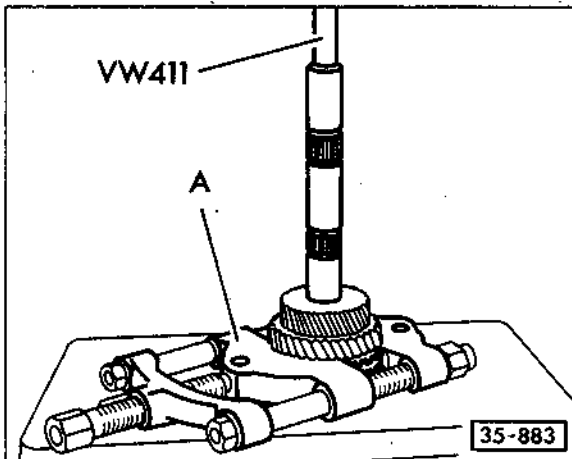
Zahnrad für 4. Gang mit Schaltrad für 3. Gang abpressen
